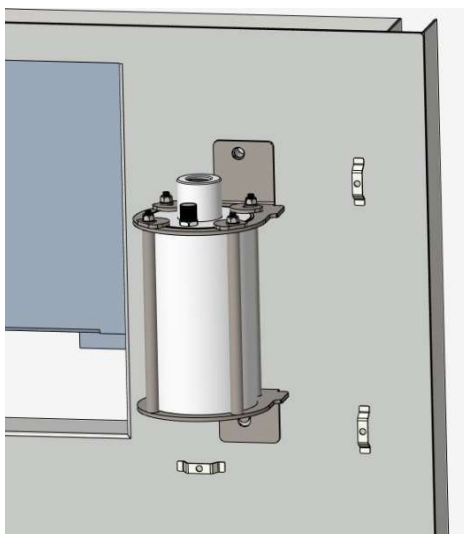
35 Ubicación de instalación del dispositivo extintor
